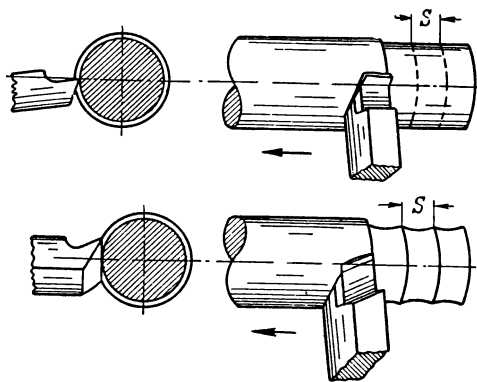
Широкий резец для чистового точения конструкции ЛПИ им. М. И. Калинина.
